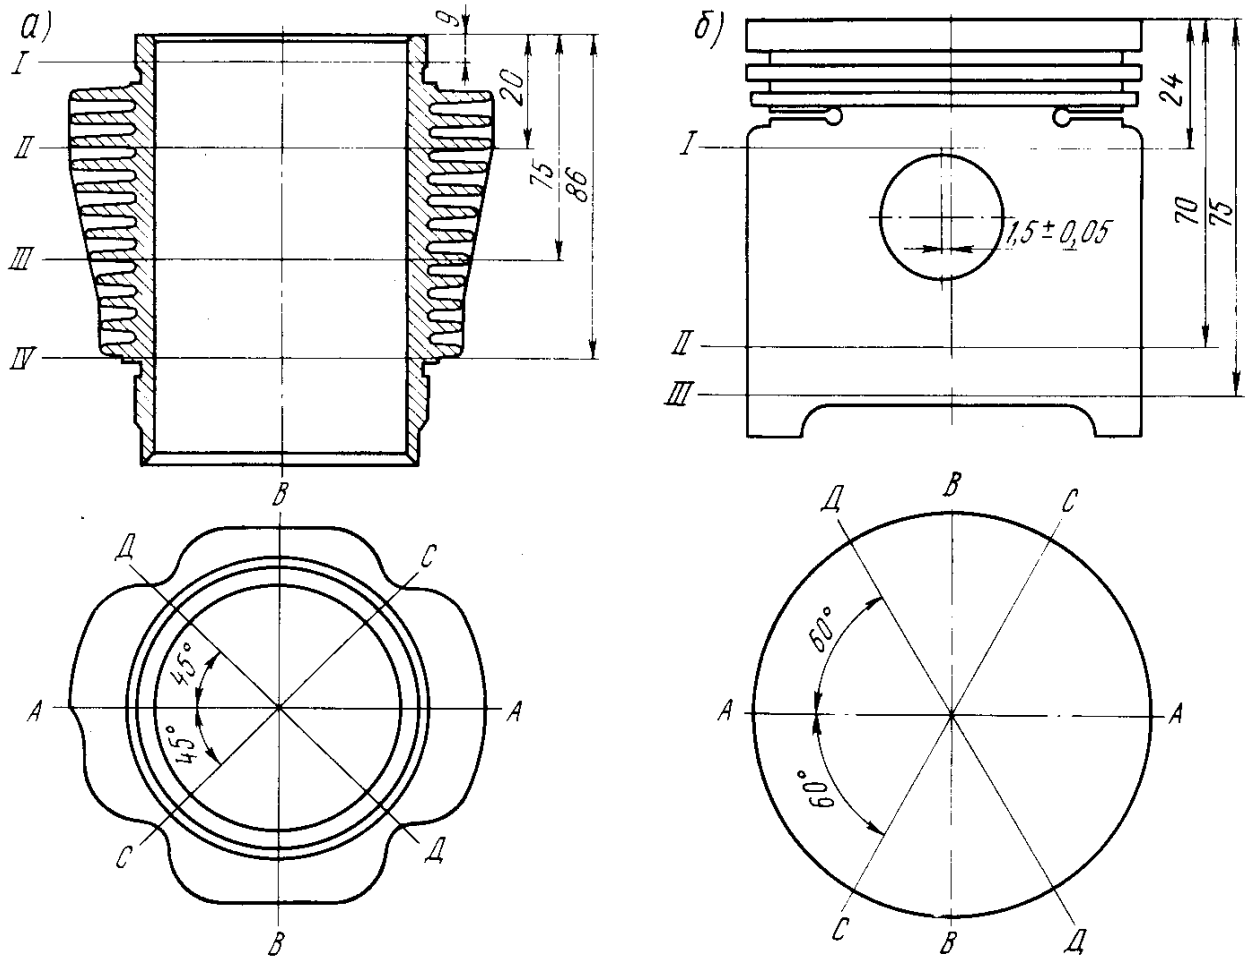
Схема замеров цилиндра и поршня: а—замеры диаметра зеркала цилиндра; б—замеры юбки поршня; В—В—ось коленчатого вала
